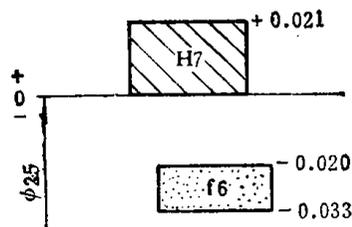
中间轴轴径和齿轮衬套内孔的公差带图
